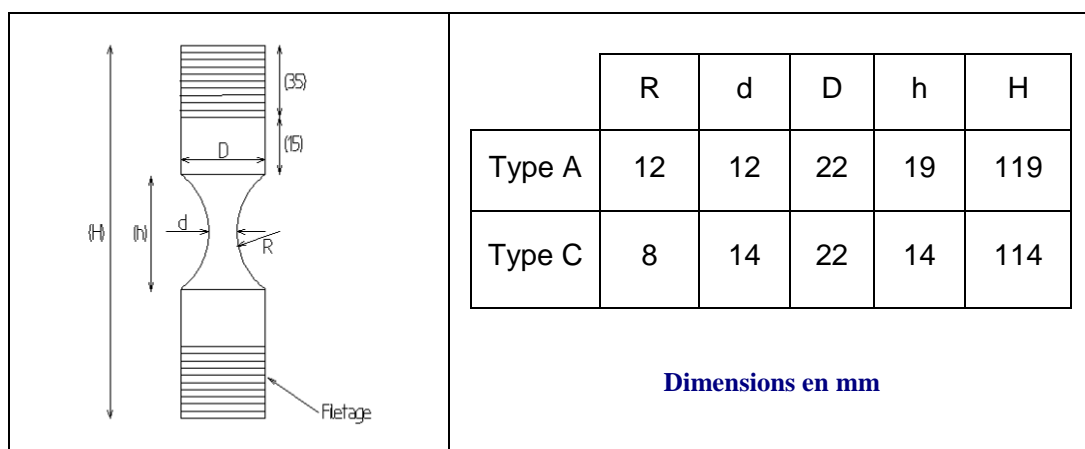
Géométrie et dimensions des éprouvettes de type « diablo »
